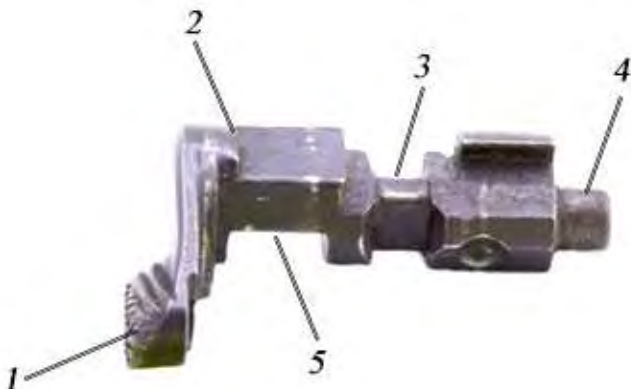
Переводчик-предохранитель: 1 – флажок; 2, 4 – цапфы; 3 – шейка; 5 – вырез
